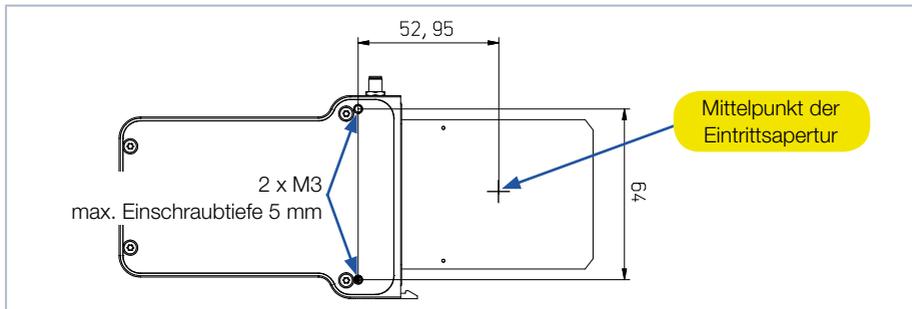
Befestigungsgewinde, Ansicht von unten
